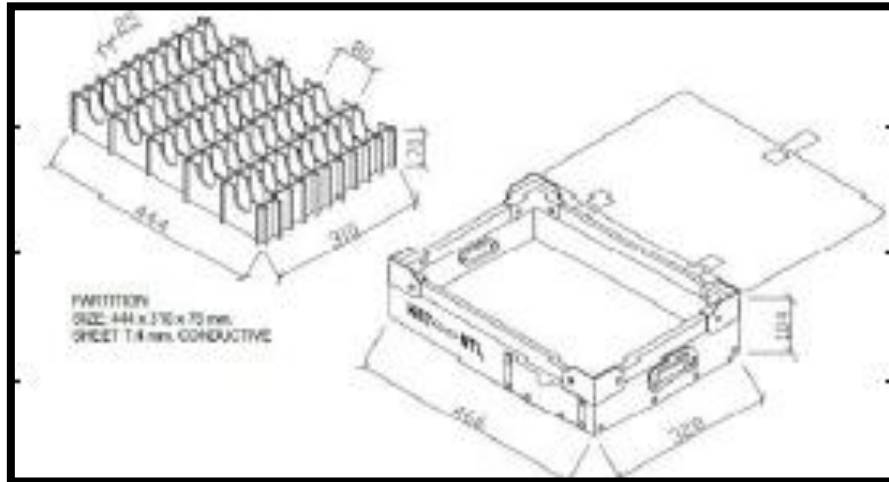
รูปแบบบรรจุภัณฑ์ PCB SUB
